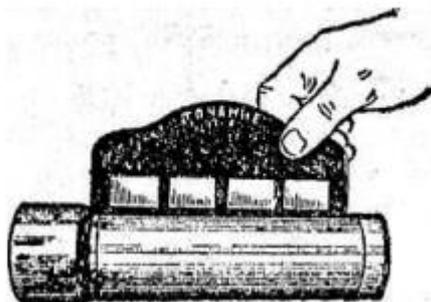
Измерение шероховатости поверхности детали эталонами.
